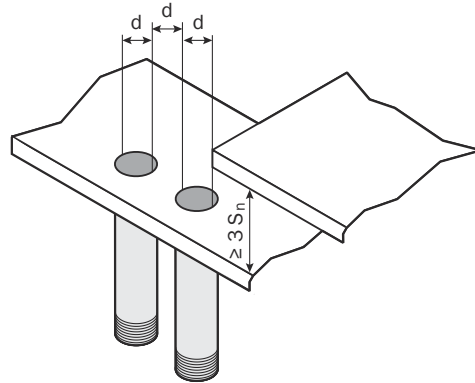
Condiciones de montaje, variantes de montaje engrasado
